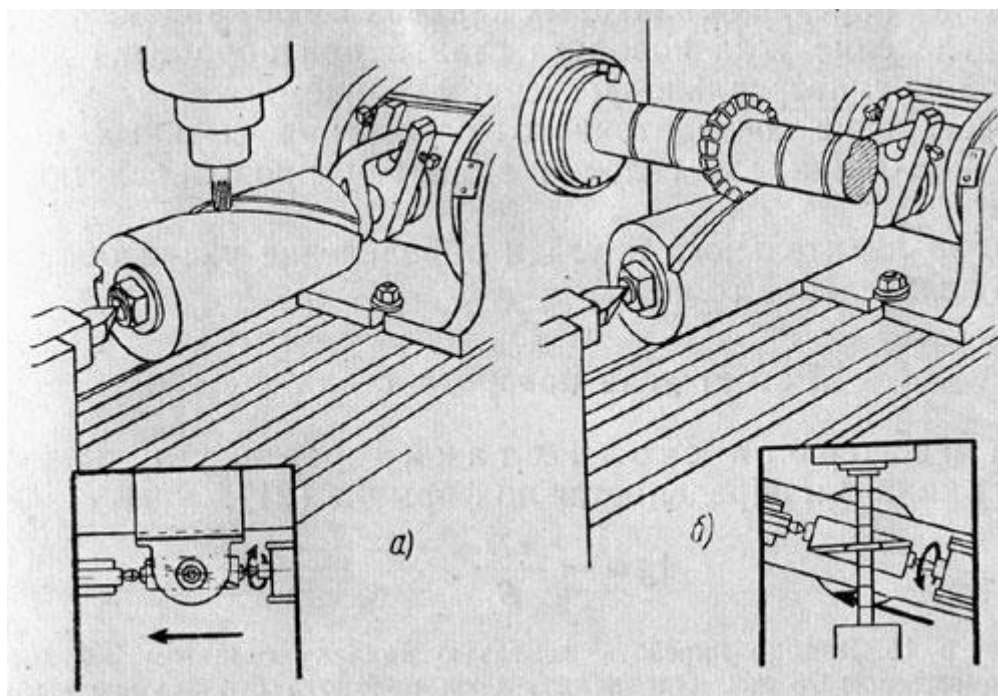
Фрезерування гвинтових канавок:
